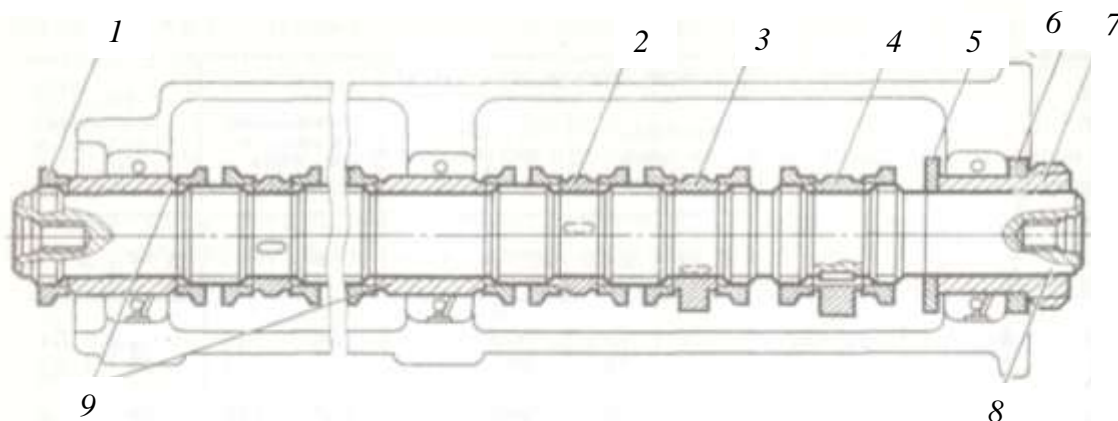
Розподільний вал ЕУТ Д49: 1- гайка; 2, 3, 4 - відповідно впускний, випускний та паливний кулачки, які працюють на два циліндри лівого та правого рядів; 5,6 – кільця опорно-упорної шийки, 7 – приводна втулка; 8 – тіло валу; 9 – втулка
